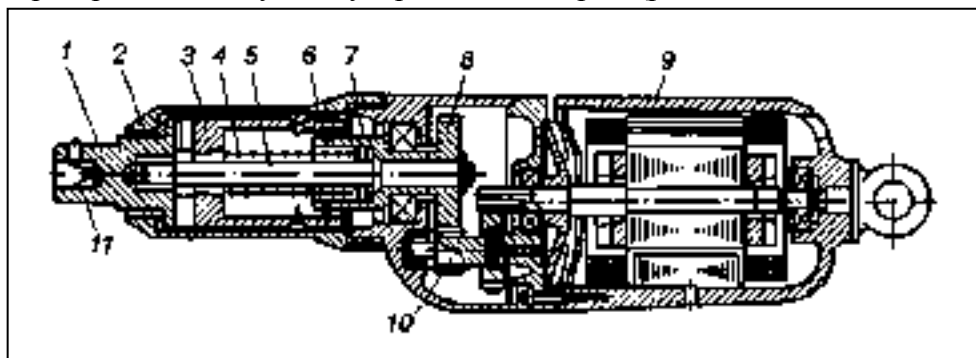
Ударно-импульсный электрогайковерт: 1 — рабочий наконечник; 2 — втулка; 3 — ведомая полумуфта; 4, 11 — пружины; 5 — шпindel; 6 — шарик; 7 — ведущая полумуфта; 8, 10 — зубчатые колеса; 9 — корпус
